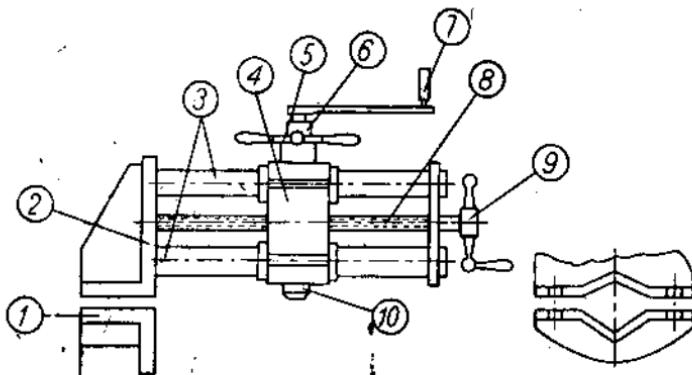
Приспособление для фрезерования шпоночных пазов на трансмиссионном валу без снятия вала с места.
